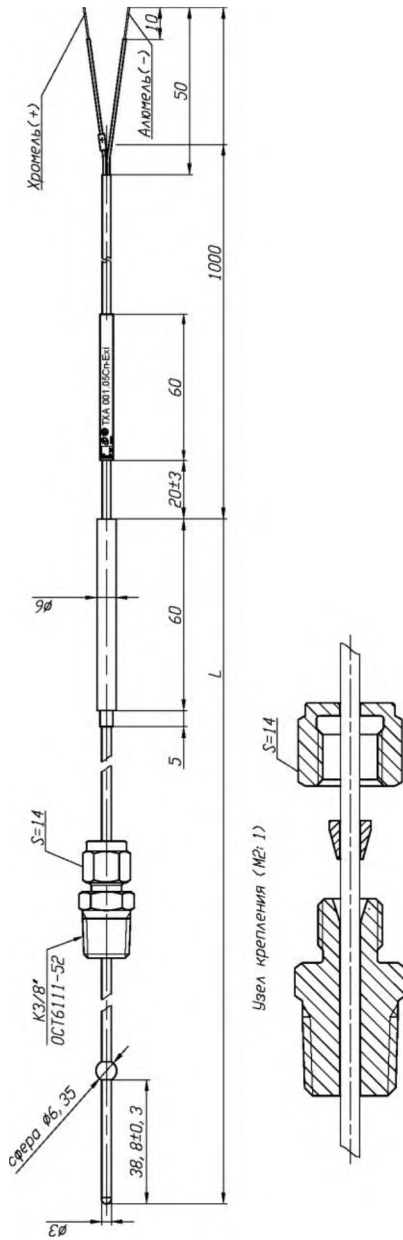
д) - Габаритный чертёж ПТ модели ТХА 001.05Сл-Ех1
